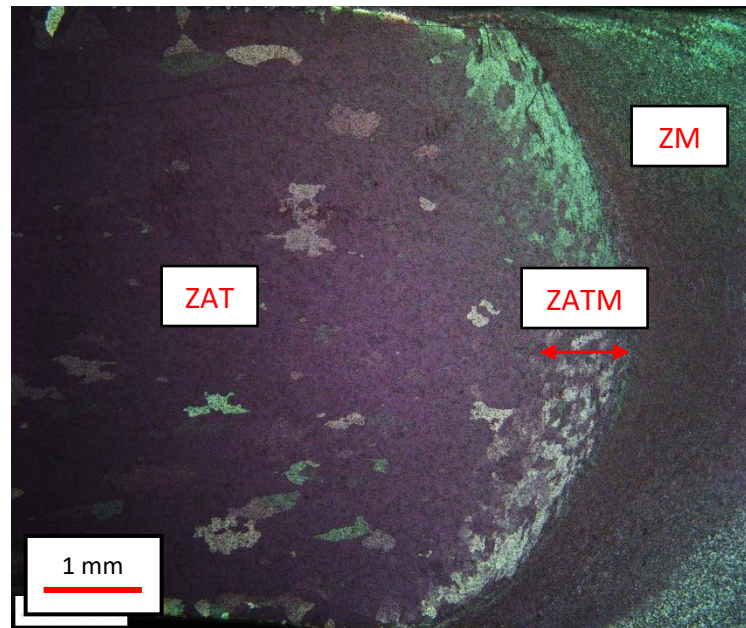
Image macroscopique d'une section transversale de la soudure par BT-FSW T4 (outil B, 800 tr/min, 700 mm/min) sous lumière polarisée (grossissement 40X)
